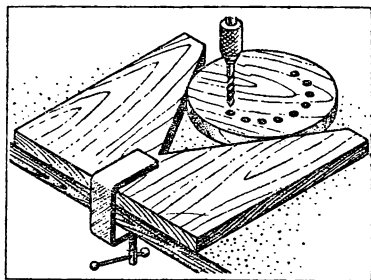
Упор для сверления отверстий в круглых заготовках.
